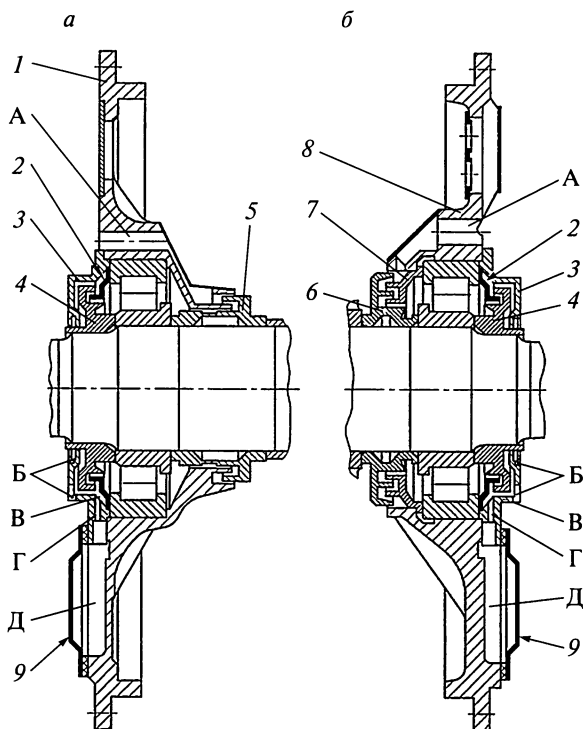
Подшипниковый узел № 2 тягового двигателя НБ-514Е:
